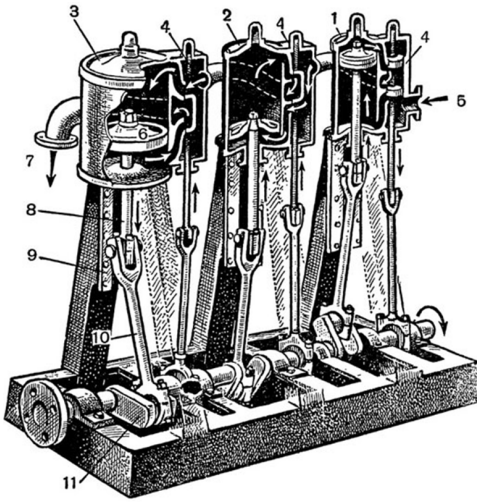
Паровая машина с тройным расширением пара: 1 — цилиндр высокого давления; 2 — цилиндр среднего давления; 3 — цилиндр низкого давления; 4 — золотниковые коробки; 5 — подвод пара; 6 — поршень; 7 — отвод пара в конденсатор; 8 — шток; 9 — параллели; 10 — шатун; 11 — коленчатый вал
